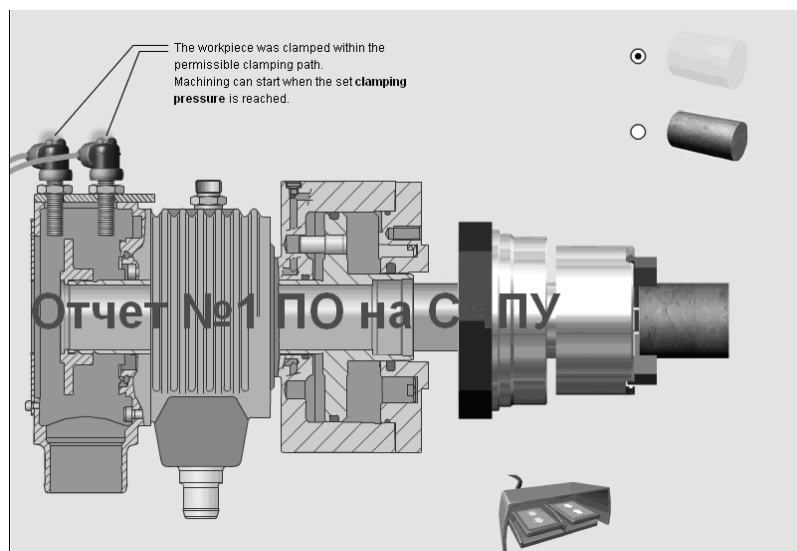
Закрепление заготовки на токарном станке с ЧПУ
